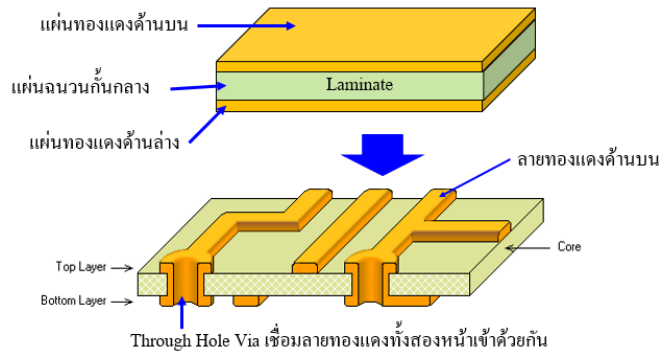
เมื่อออกแบบ PCB เสร็จแล้ว ก็ส่งไฟล์เกอร์เบอร์ (Gerber File) ไปให้ผู้ผลิต PCB
